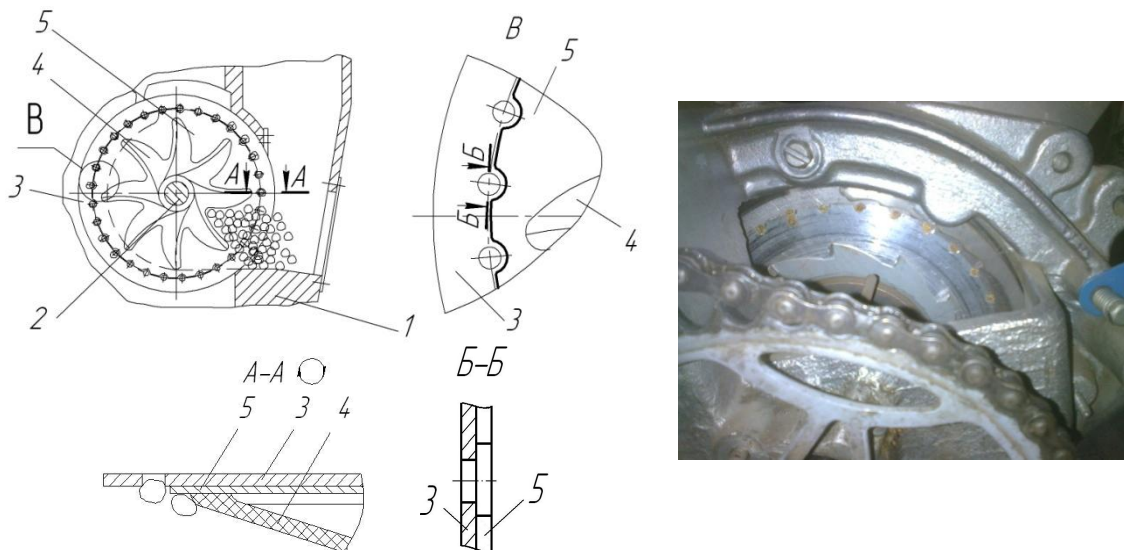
Удосконалений пневмомеханічний висівний апарат УПС-8: 1 – корпус, 2 – привідний вал, 3 – висівний диск, 4 – ворушилка, 5 – додатковий диск
